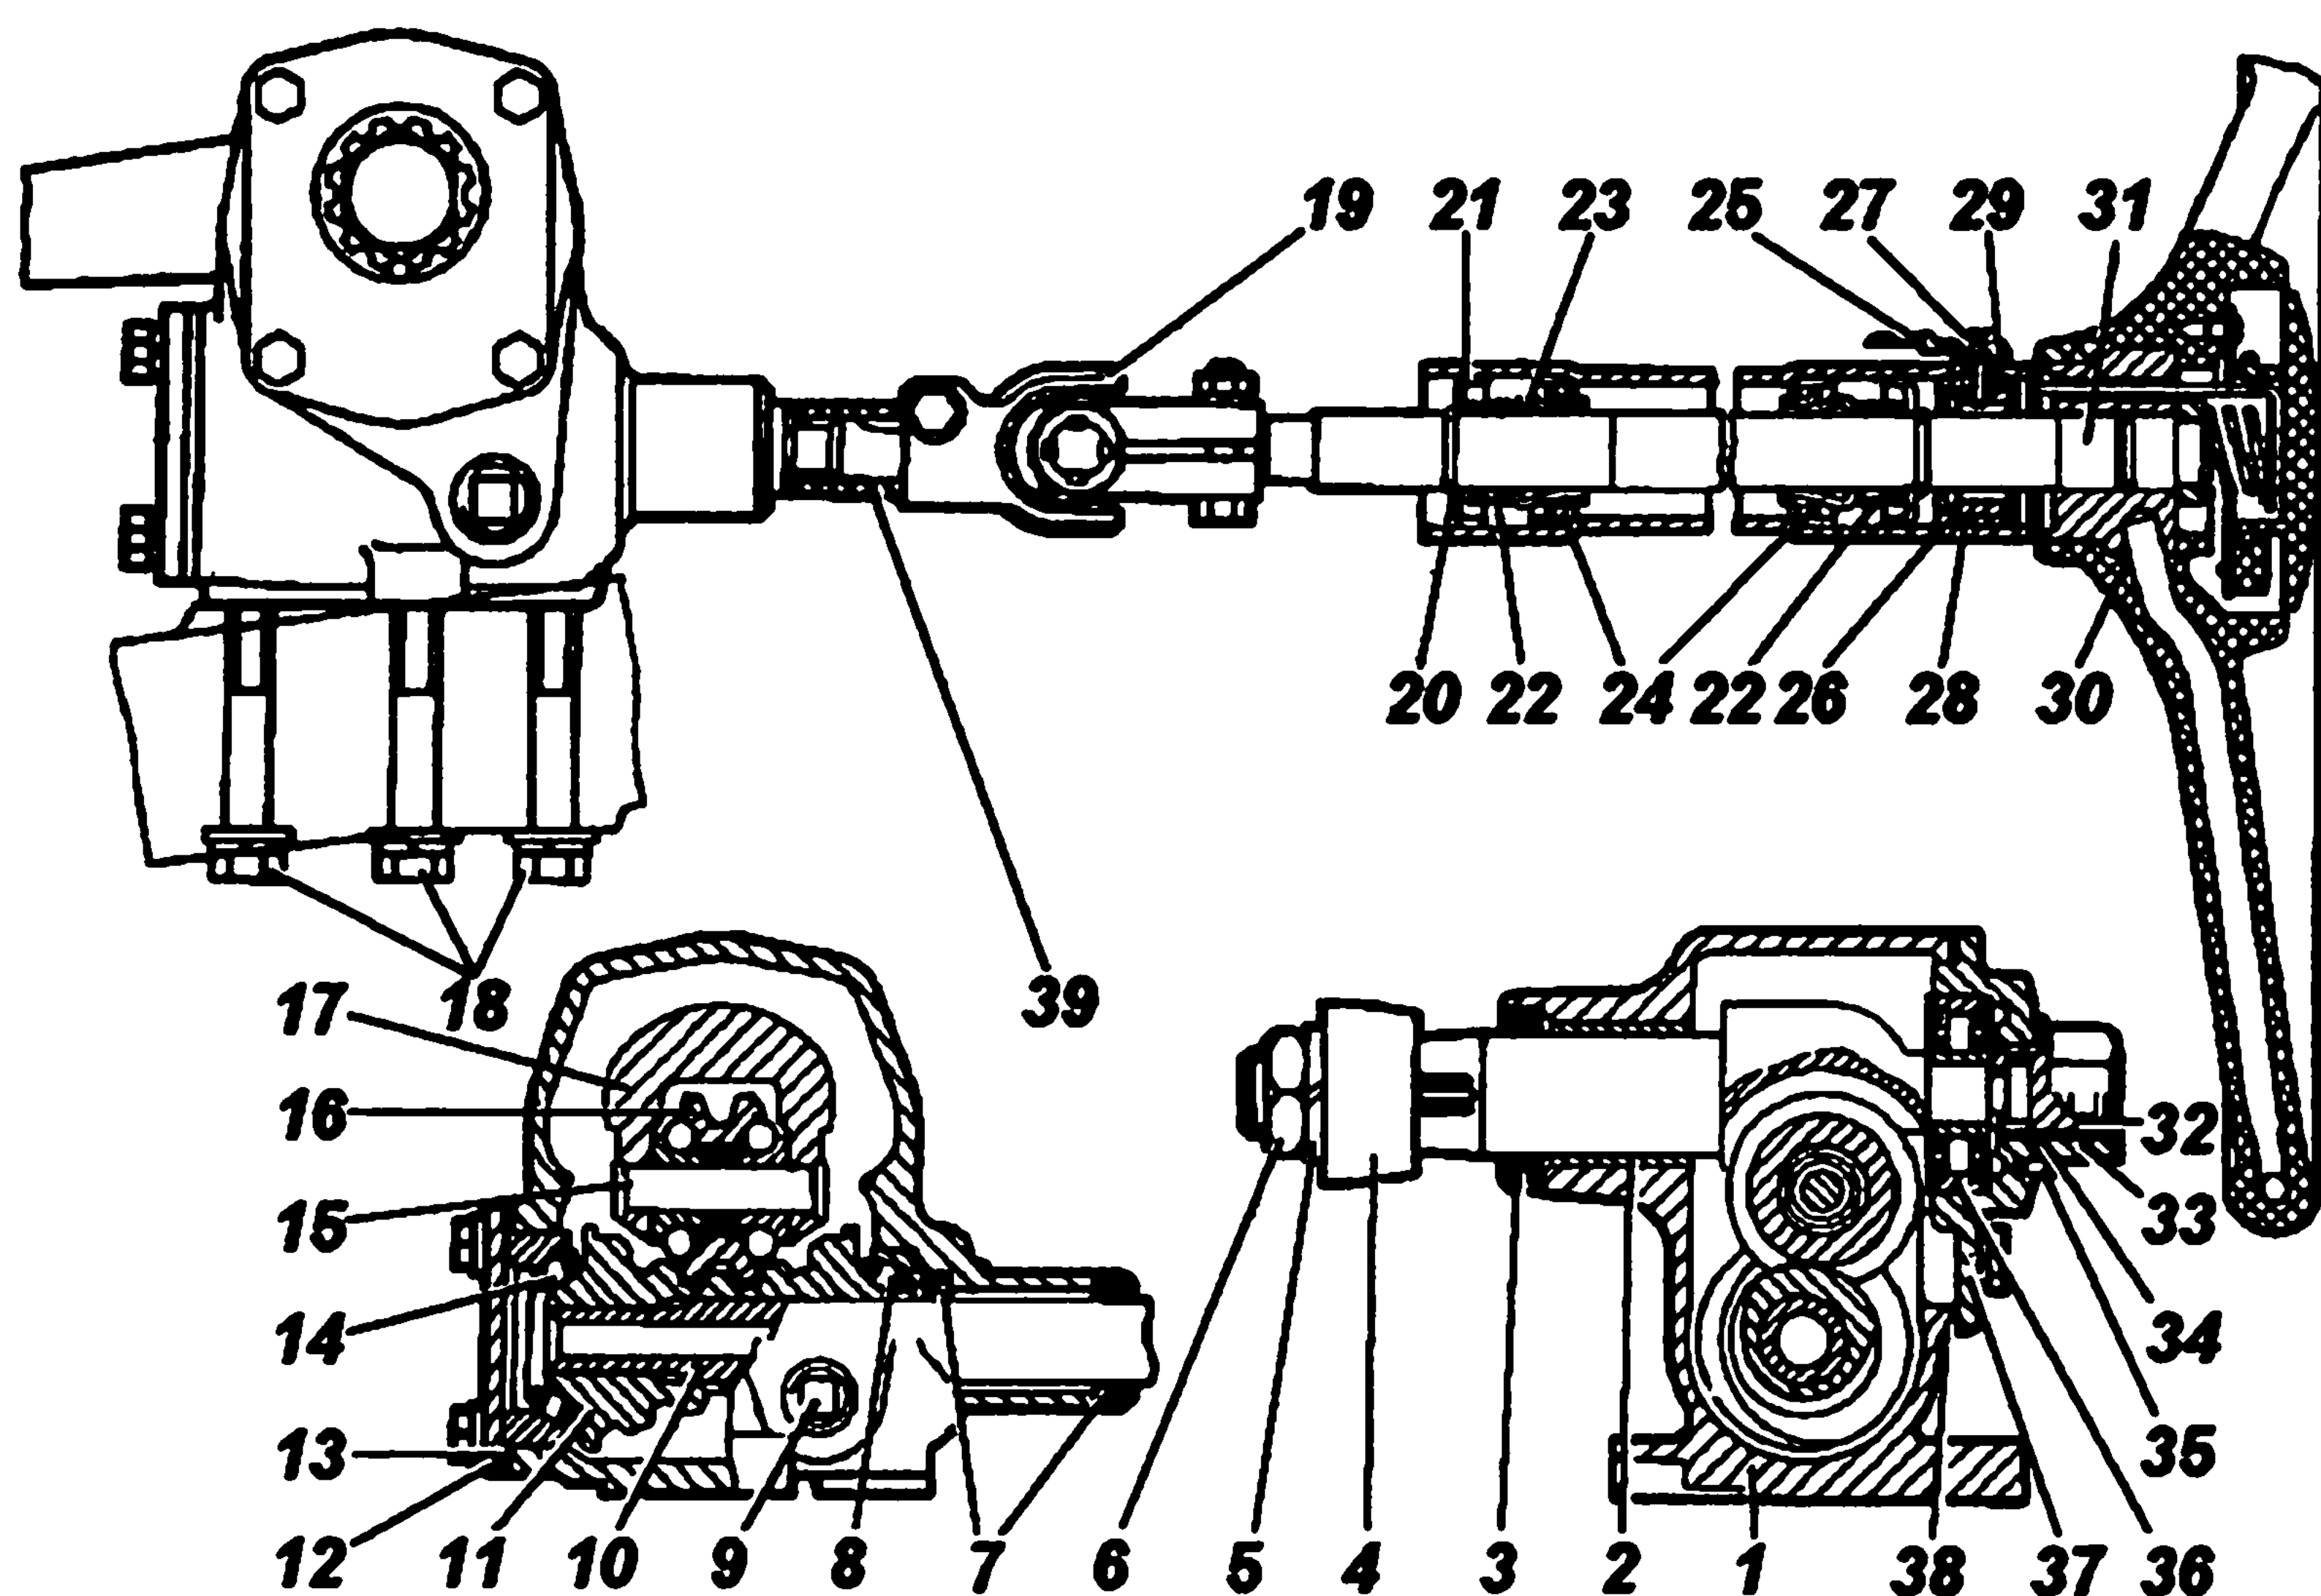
Рулевой механизм типа глобоидальный червяк с двухгребневым роликом:
